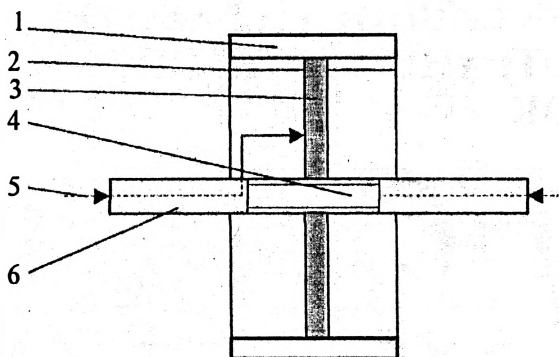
Конструктивная схема пневмомотора: 1 – вращающийся цилиндр (ходовое колесо, барабан и т.п.); 2 – шлицы на 1 для передачи крутящего момента; 3 – поршень; 4 – правая, левая нарезки с переходными канавками на неподвижном валу 6; 5 – подача воздуха.
